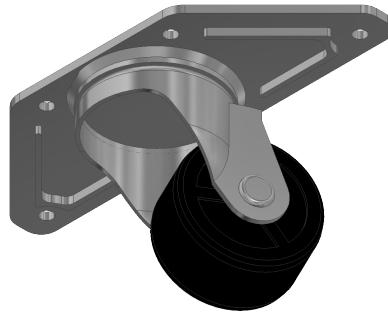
Llanta utilizada en el ensamble del cajón 1.
